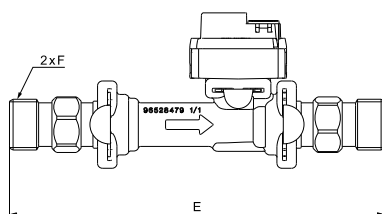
Abmessungen des Sensors VFS 1-20 l/min (mit Adaptern)
